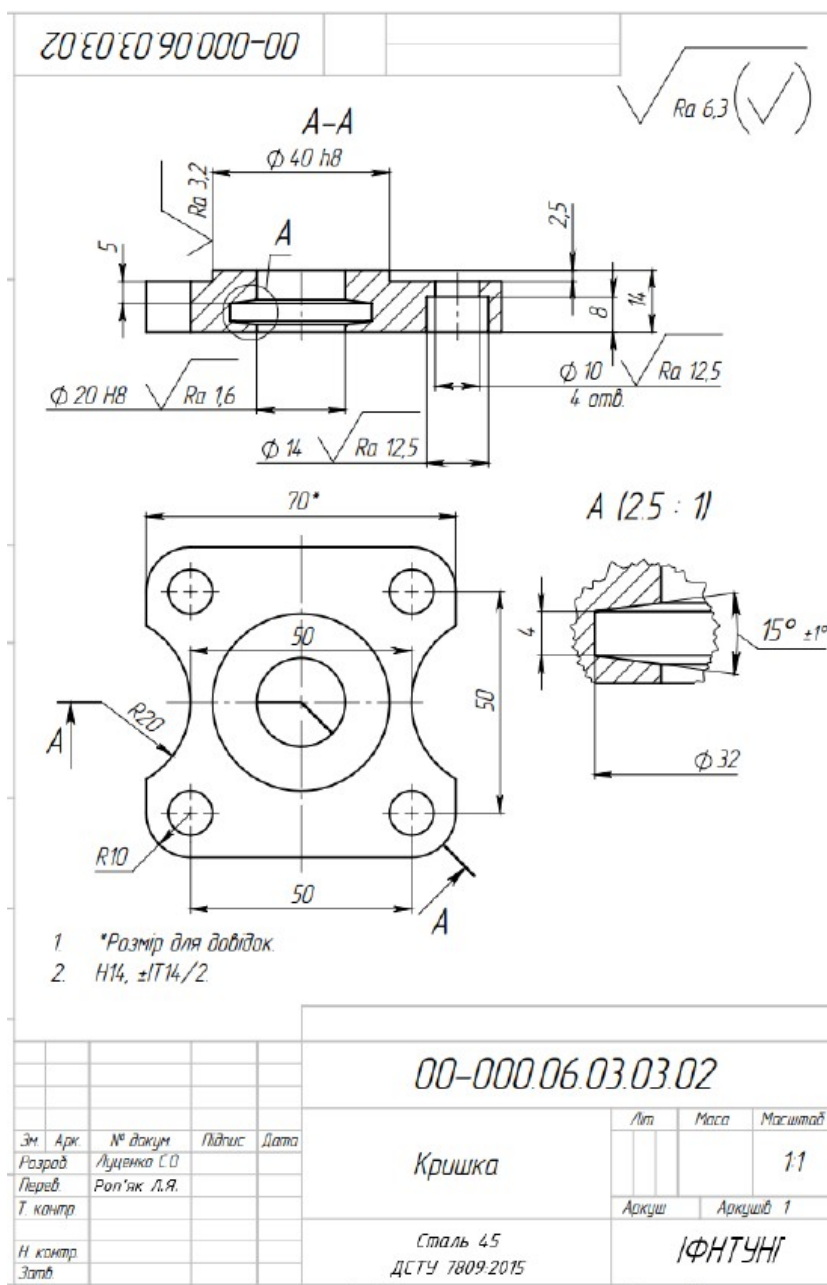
Креслення деталі Кришка 00.000.06.03.03.02
